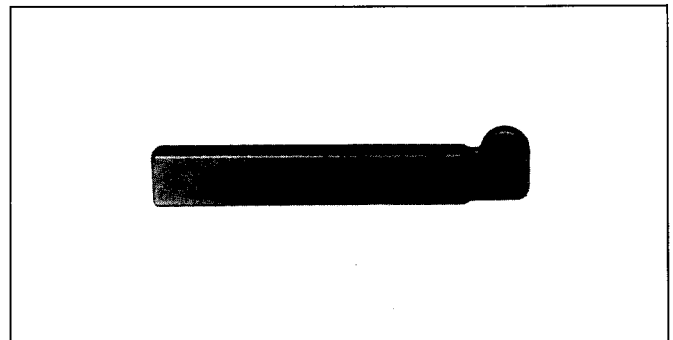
Gesenkschmiedeter Klinkenhebel (1,1 kg) aus 37 Cr 4 V zum Schließen von Druckgießwerkzeugen
